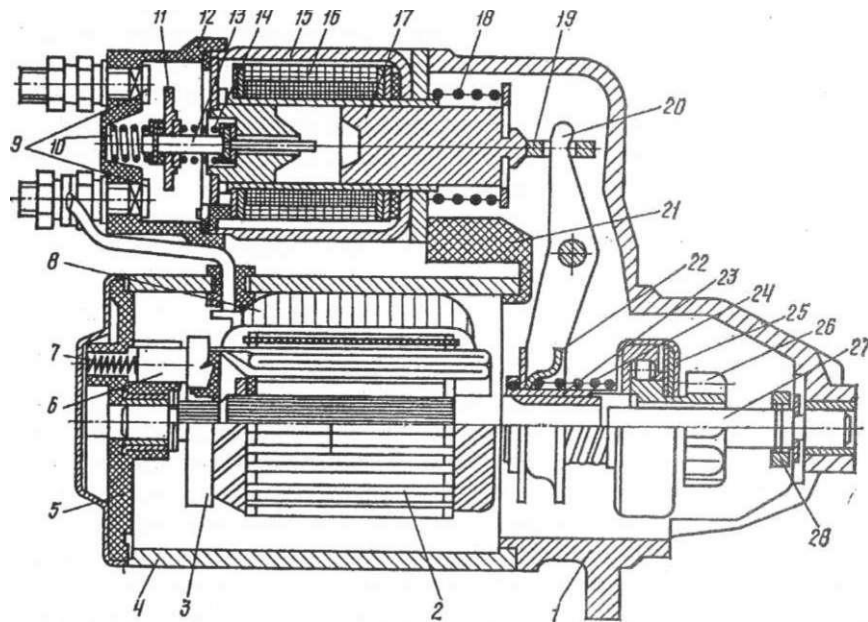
Стартер СТ-362 тракторного пускового двигуна ПД-10УД: 1 - кришка з боку привода; 2 - якір; 3 - торцевий колектор; 4 - корпус; 5 - кришка з боку колектора; 6 - щітка; 7 - пружина щітки; 8 - полюс статора з обмоткою збудження; 9 - силові контакти; 10 - пружина штоку; 11 - контактний диск; 12 - кришка тягового реле; 13 - шток; 14 - прижимна пружина; 15 - корпус реле; 16 - котушка тягового реле; 17 - якір тягового реле; 18 - пружина; 18 - серга; 20 - важіль включення стартера; 21 - ущільнююча прокладка; 22 - муфта включення; 23 - втулка; 24 - пружина включення; 25 - муфта вільного ходу; 26 - шестерня включення; 27 - вал якоря; 28 - упорна шайба
